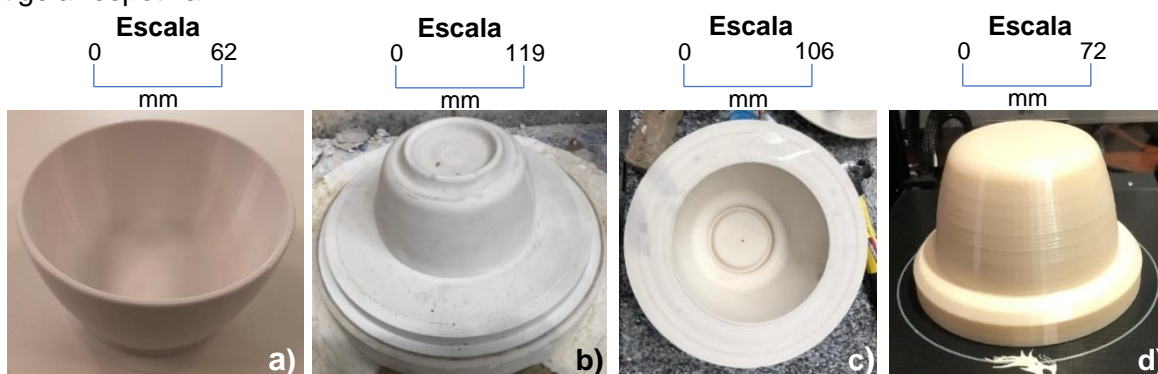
Componentes necessários para a conformação Roller da tigela do projeto: a) segunda impressão 3D da tigela; b) madre de gesso; c) molde de gesso e d) calibrador impresso em 3D.
